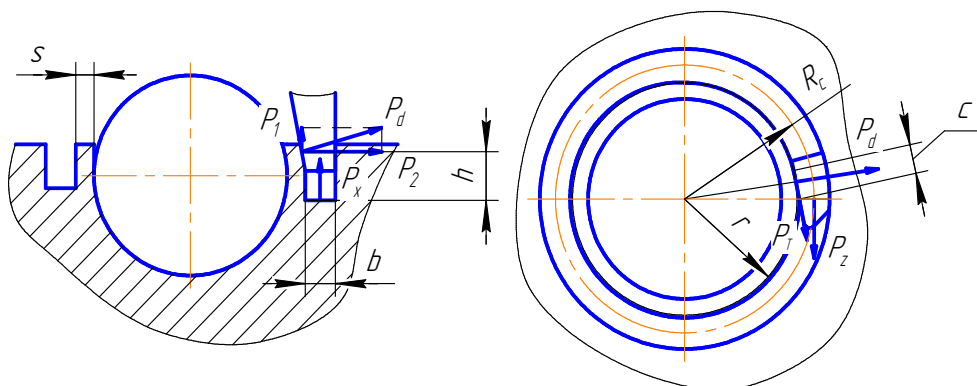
Схема для розрахунку інструмента для завальцювання кульки
